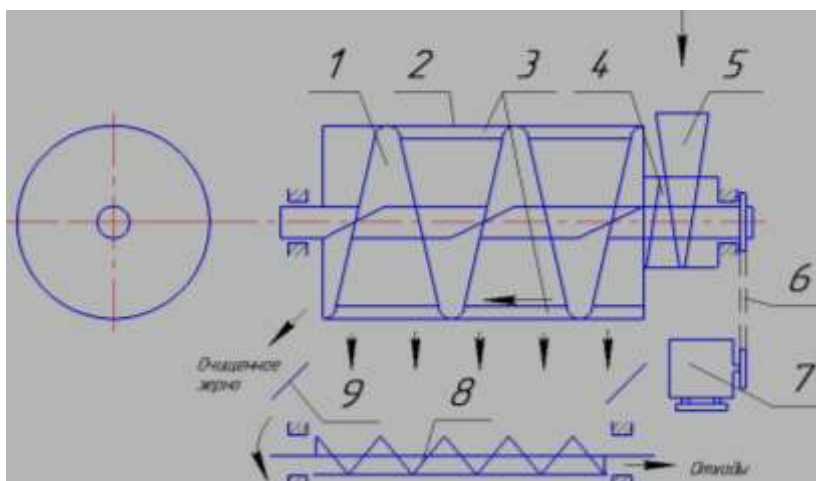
Схема цилиндрического решета с транспортирующей спиралью
